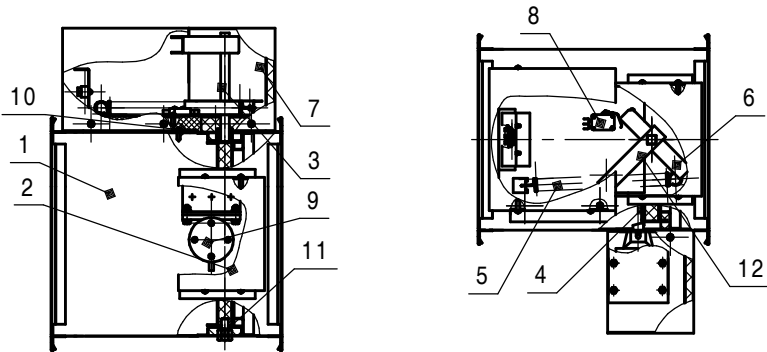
Установочные, габаритные и размеры внутреннего сечения клапана BM
